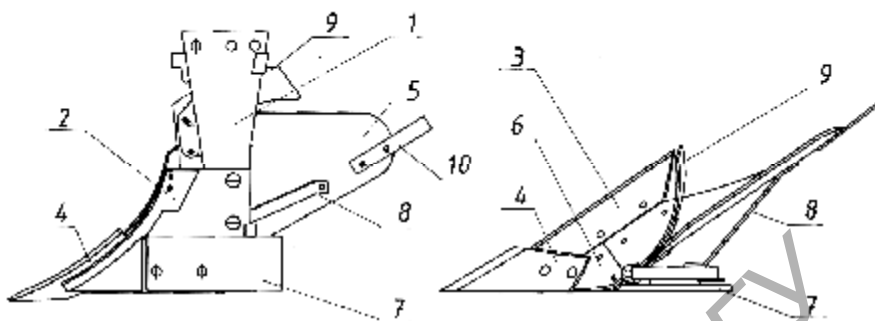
Лемешно-отвальный корпус ПЛП-01 с полувинтовым отвалом и углоснимом:
